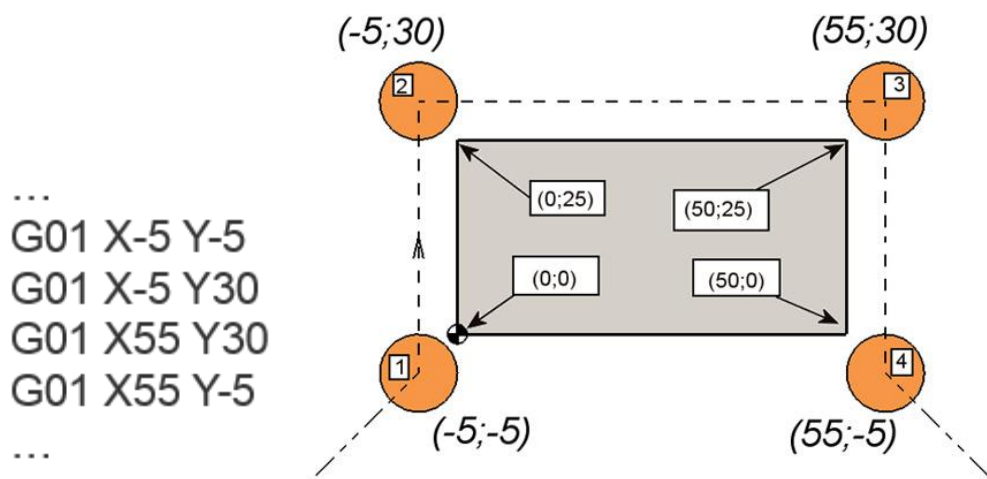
Траєкторія обробки заготовки фрезою 10 мм
